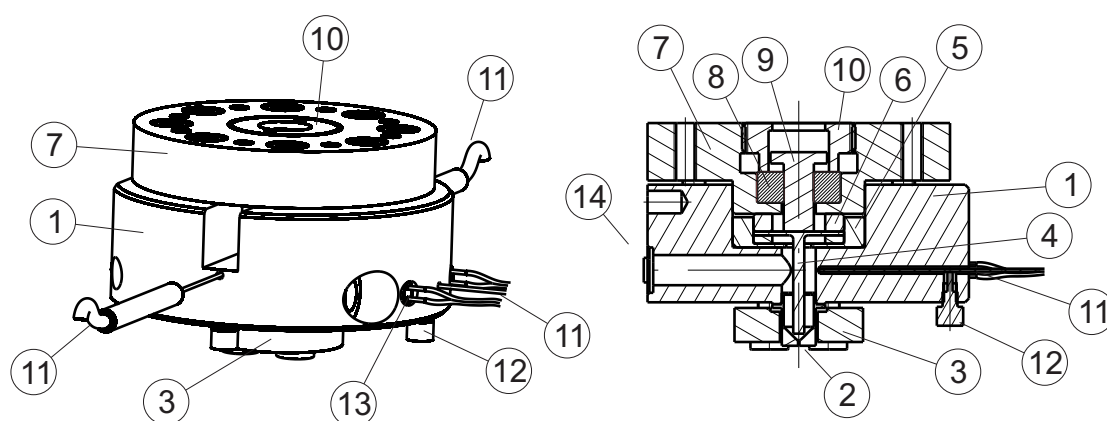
Konstruktion des Halters in isometrischer Darstellung und Schnittdarstellung mit Halter (1) zur Lagerung der Düse (2), montiert über eine Düsenklemmplatte (3) und Aufnahme für das flexible Element (4), gelagert in einem Träger (5) mit Klemmscheiben (6). Axiale Fixierung über eine Kraftlenkscheibe (7), in der über eine Gleitlagerbuchse aus Graphit (8) ein Zentrierstößel (9) geführt wird und mit einem Deckel (10) gesichert wird. Temperatursensoren (11) mit Fixierungsschrauben (12) zur Temperaturüberwachung bei Aufheizung durch Heizpatronen (13). Über die Schnittstelle (14) wird der Halter an die Fluidzufuhr angebunden.
